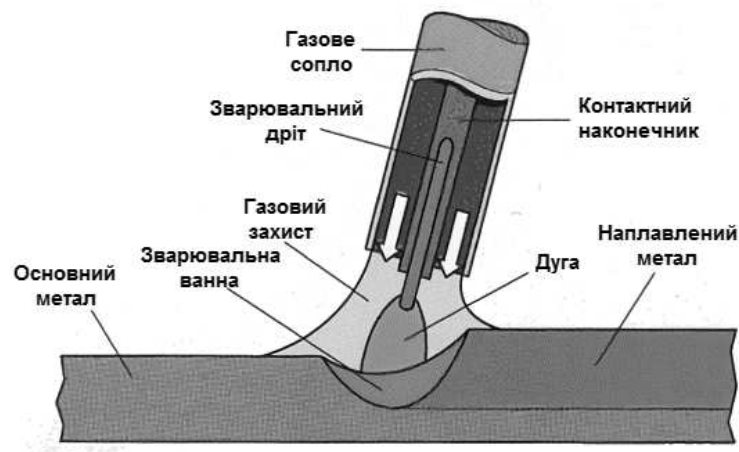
Схема GMAW-способу наплавлення [28]
